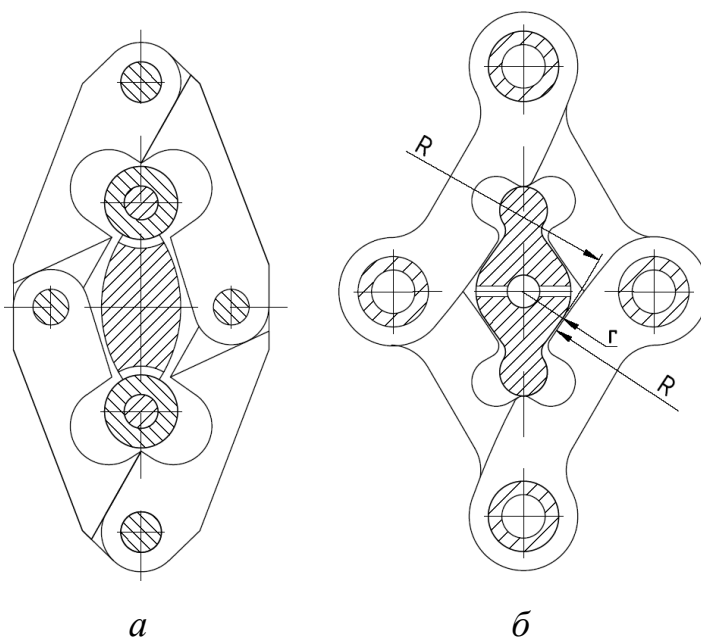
Конструктивні схеми шарнірного чотирикутника та регулюючого кулачка: *а* – кулачок з рухомими роликками; *б* – цільний кулачок з округленими опорними вершинами
